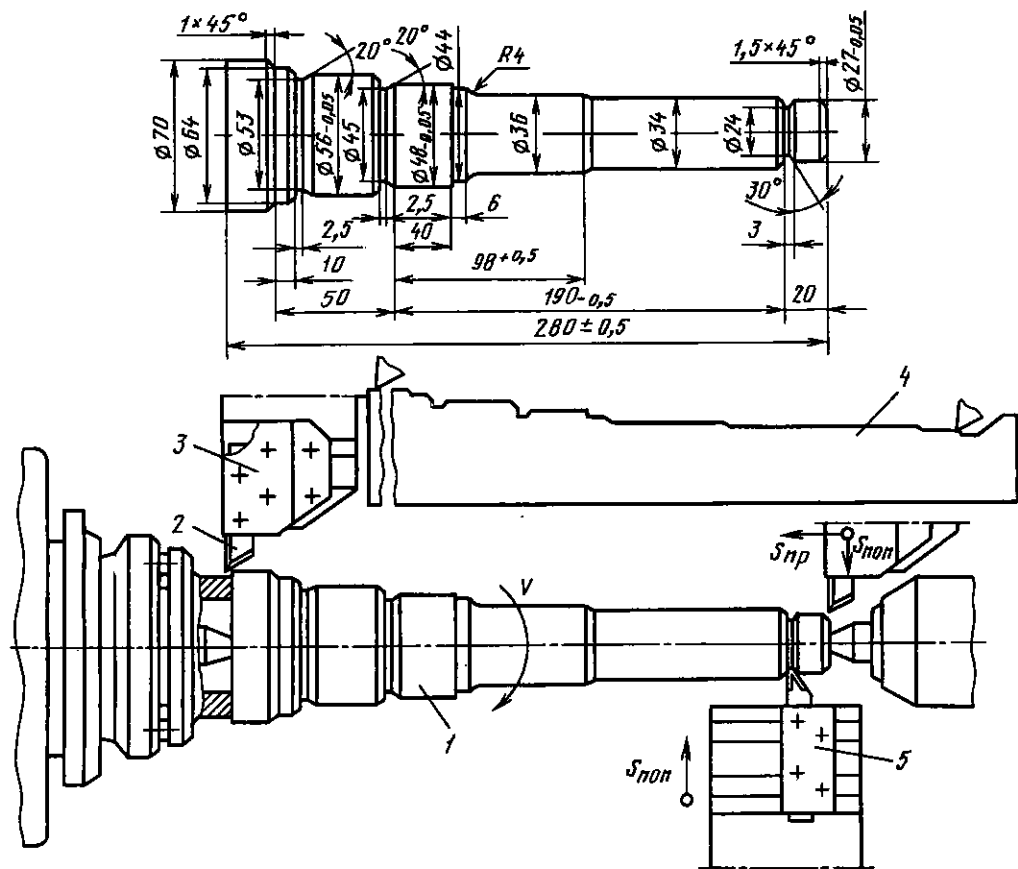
Схема обработки детали на одношпиндельном копировальном полуавтомате: 1 – заготовка; 2 – резец; 3 – копировальный суппорт; 4 – копия; 5 – поперечный суппорт
